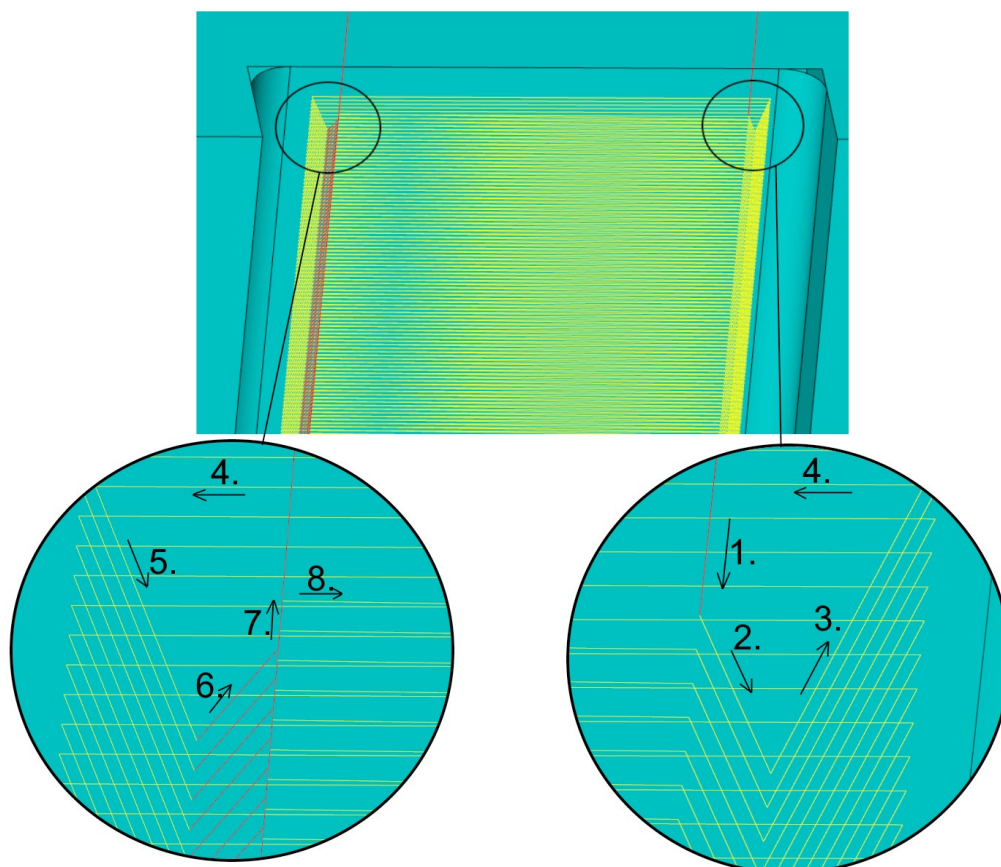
Ukázka hrubování obrobku rozdílnými metodami.
